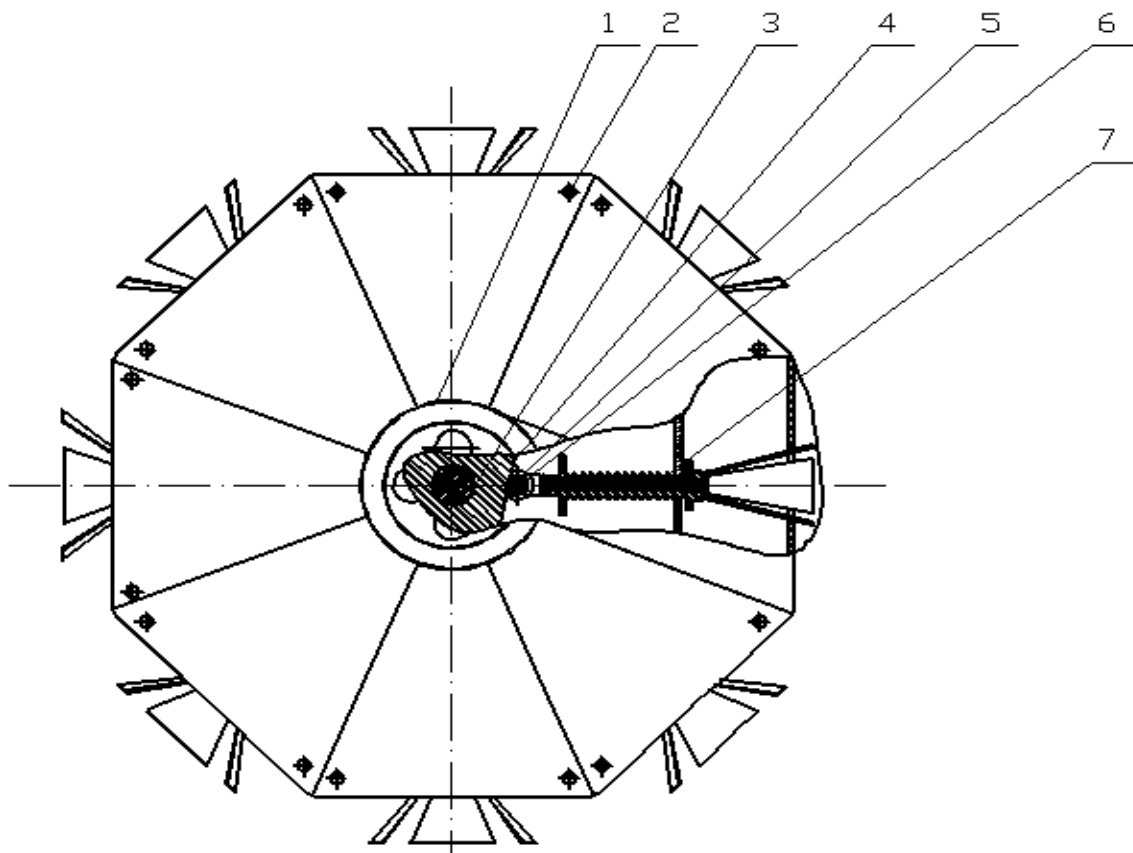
Принципова кінематична схема барабана перцеочищувальної машини: 1 – шків; 2 – кожух; 3 – вал барабана; 4 – кулачок барабана; 5 – ролик плодоутримувача; 6 – вал ролика плодоутримувача; 7 – каркас барабана
